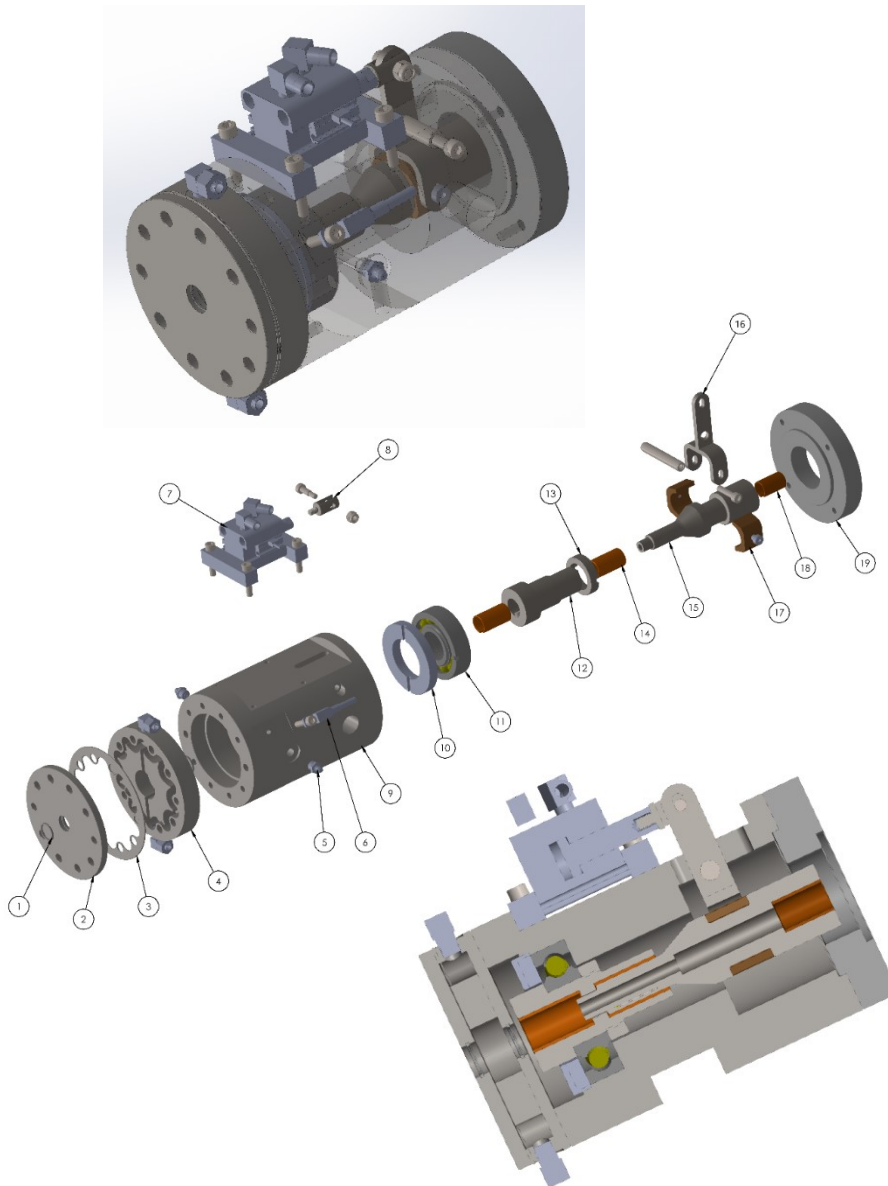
Motorização do fuso com vista explodida e vista de corte
